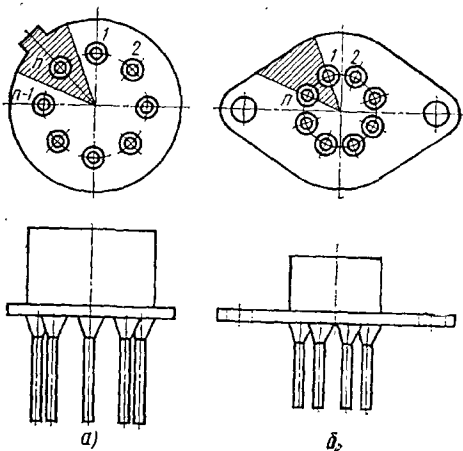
Конструкции корпусов типа 3 подтипов 31(а) и 32(б) с выводами круглого сечения
